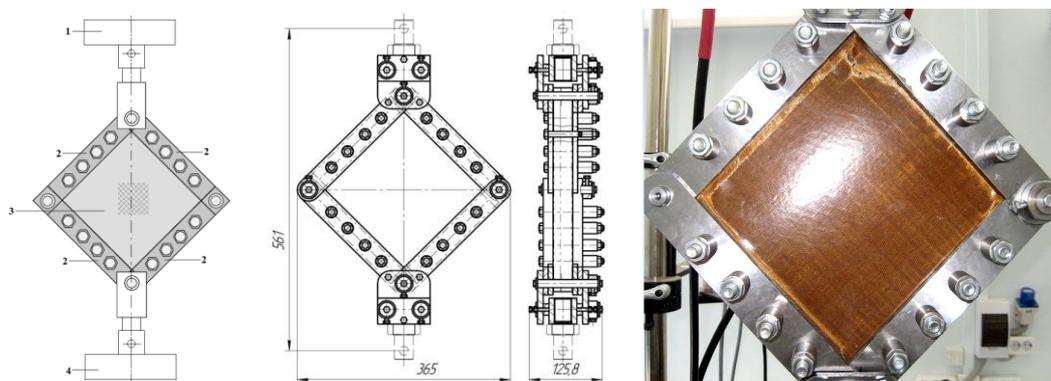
Схема закрепления, эскиз оснастки и образец-панель закреплённый в оснастке во время испытаний на сдвиг (1 –траверса; 2 – захваты (шарнирная рама); 3 – образец; 4 – основание)
